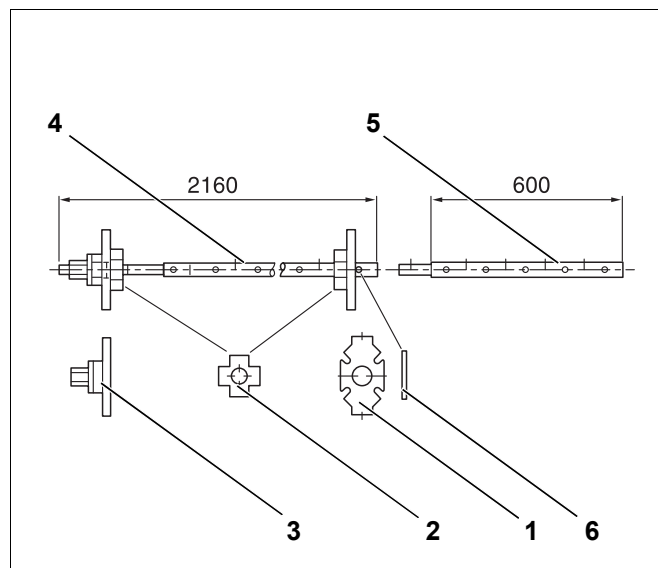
Strettoi di montaggio dimensioni 2.2 (misure in mm)
